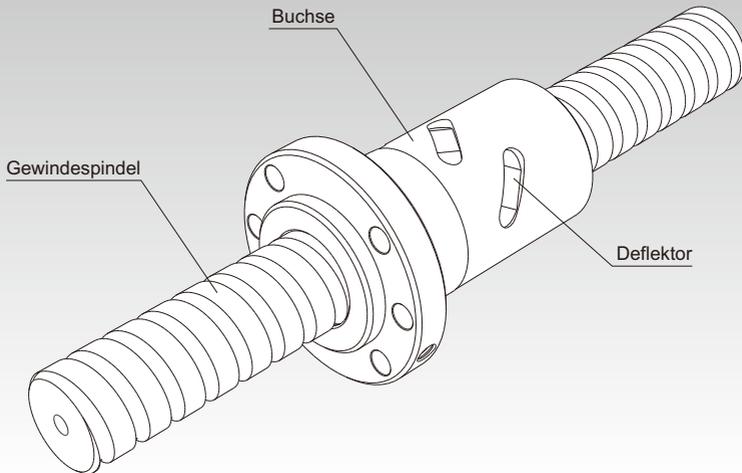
DIN-Kugelgewindetrieb (entspricht DIN 69051)
